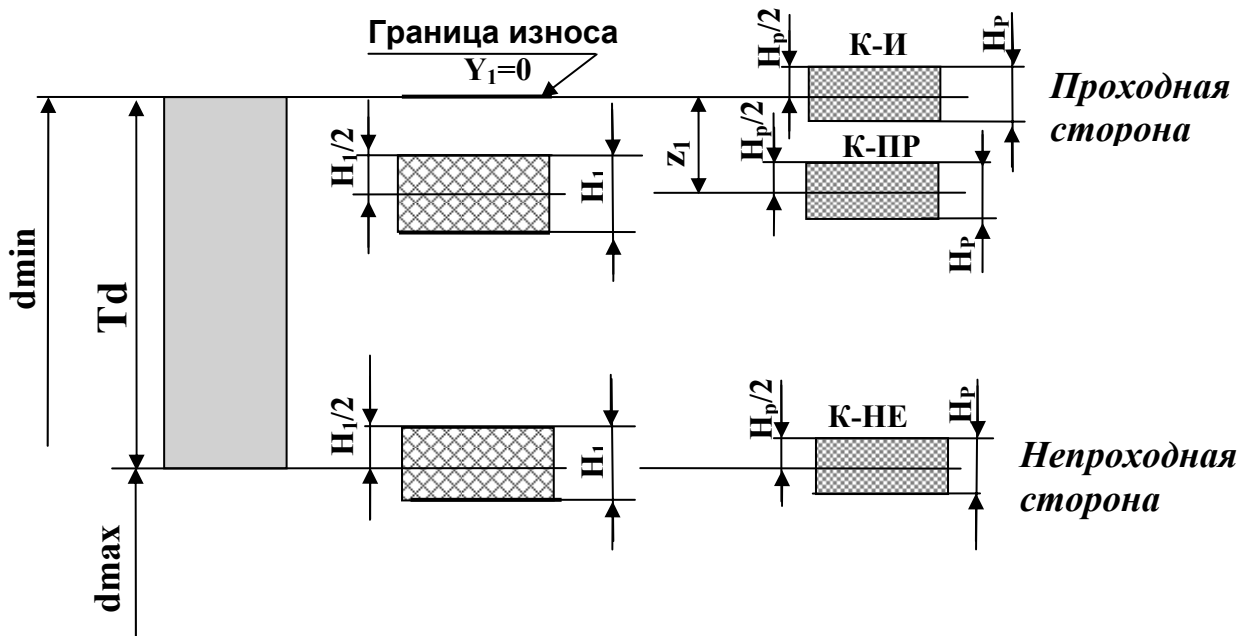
Схемы расположения полей допусков калибров-скоб и контркалибров для контроля валов номинальными размерами до 180 мм
